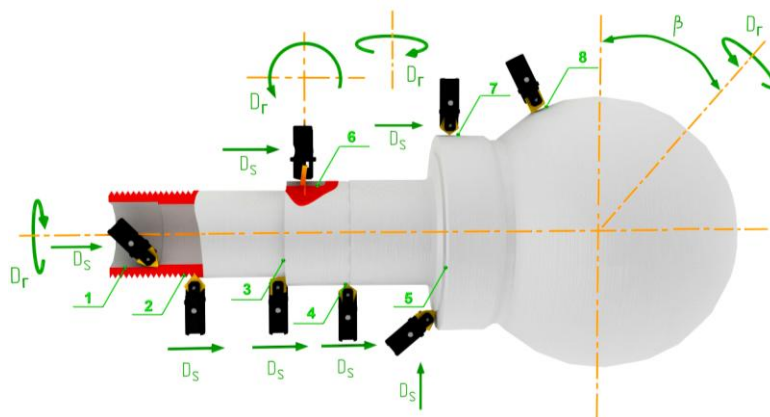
Схема обработки конструктивных элементов поверхностей деталей:
